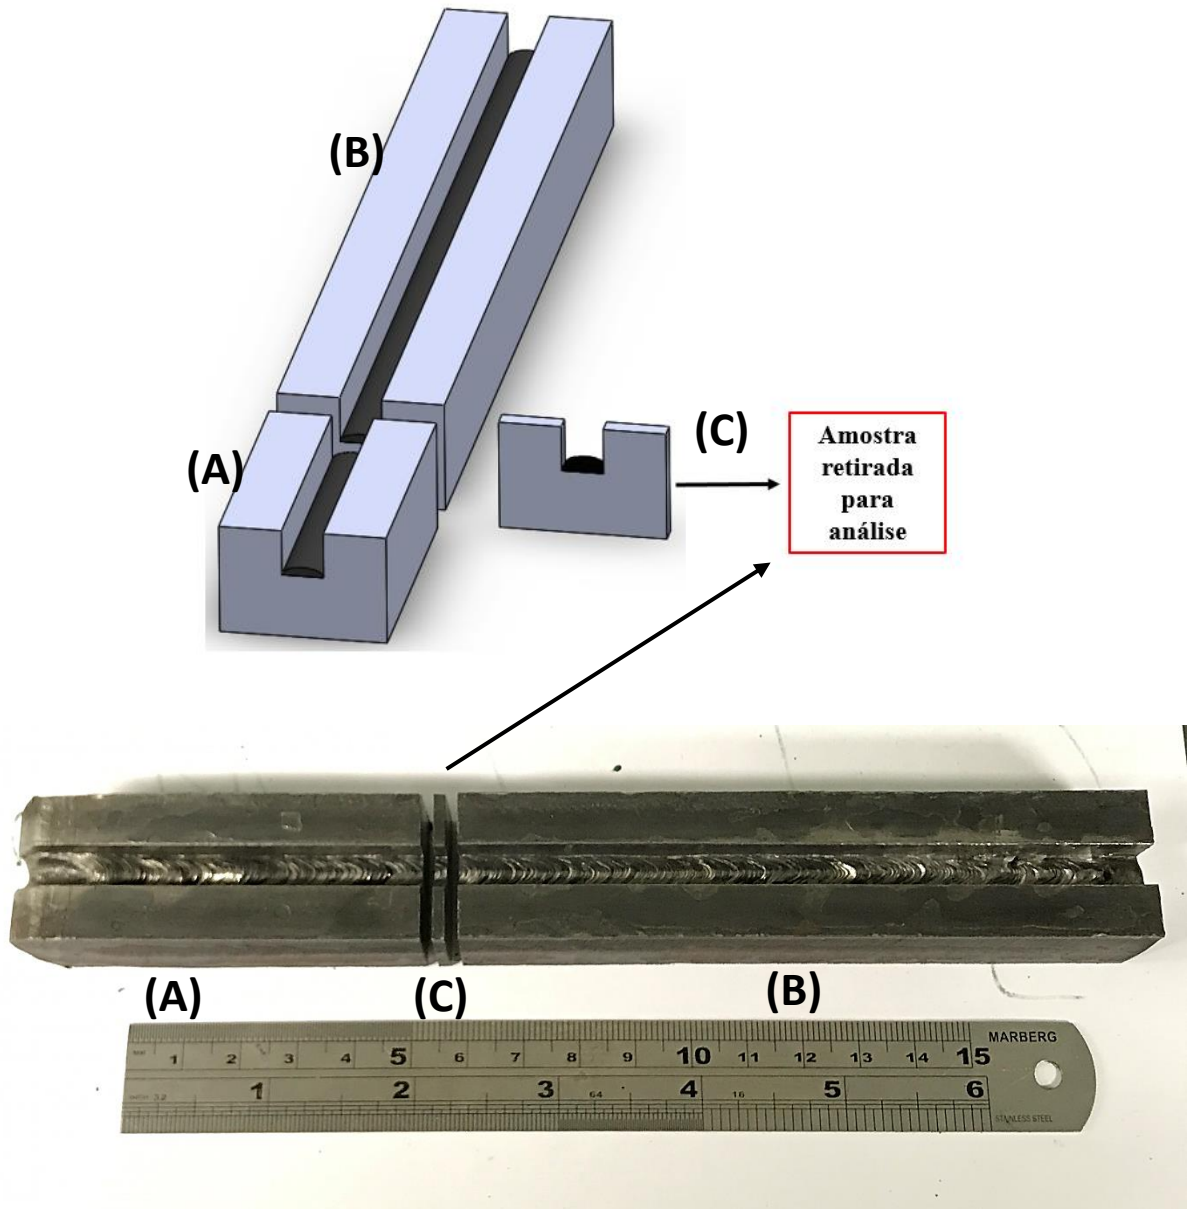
Corpo de prova cortado com destaque para a amostra retirada.
